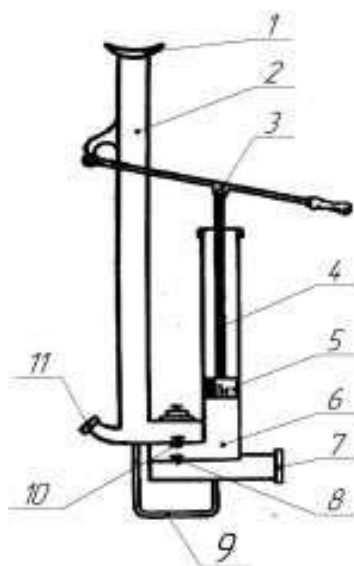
Схематичний розріз гідропульта «Милиця»: 1 – приклад; 2 – стійка; 3 – важіль; 4 – шток; 5 – поршень; 6 – піддон; 7 – звиваючий штуцер; 8 – всмоктувальний клапан; 9 – стрем'я; 10 – нагнітальний клапан 11 – викидний штуцер
